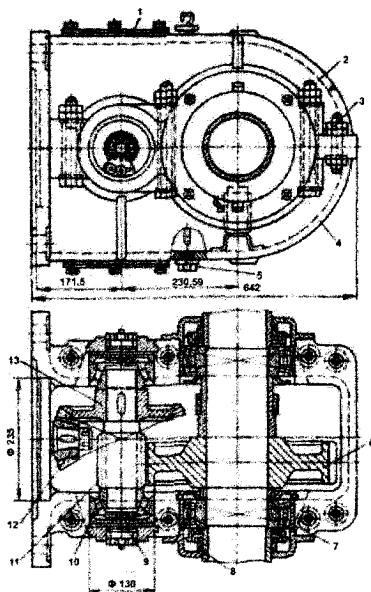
Цилиндроконический двухступенчатый редуктор: 1 – крышка редуктора с окном; 2 и 4 – две части литого корпуса; 3 – болты; 5 – пробка для слива отработанного масла; 6 – зубчатое колесо; 7 – моторно-осевые вкладыши; 8 – лабиринтное уплотнение; 9 – регулирующие винты; 10 – конические подшипники; 11 – вал-шестерня; 12 – коническая спиральнозубчатая шестерня; 13 – коническое спиральнозубчатое колесо.
